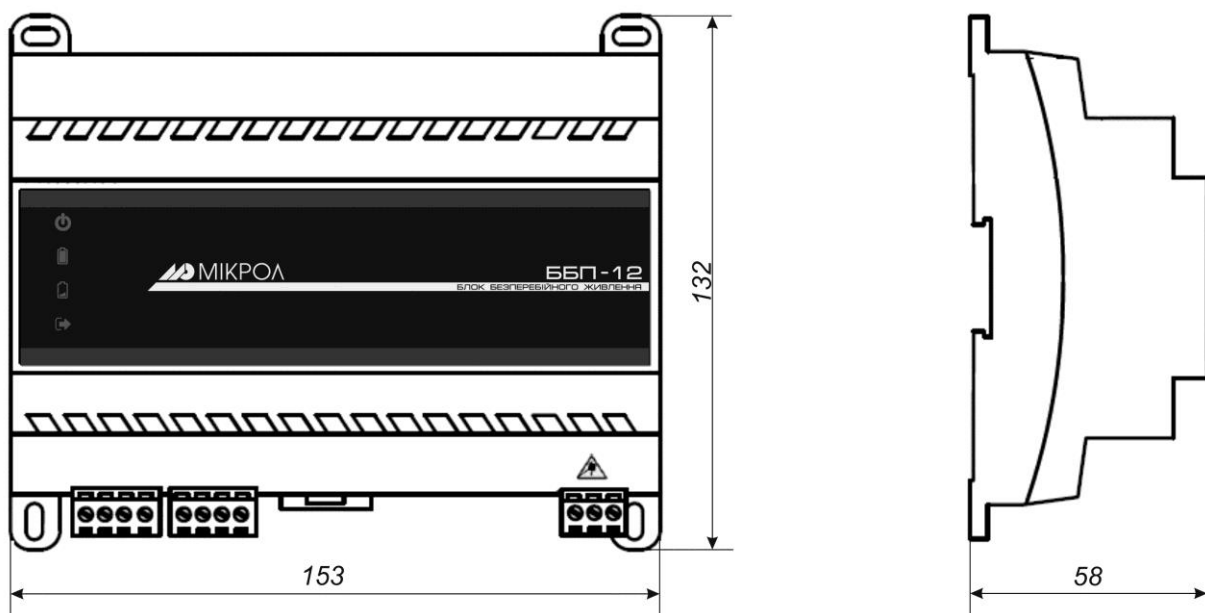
Зовнішній вигляд і габаритні розміри блоку ББП-12
